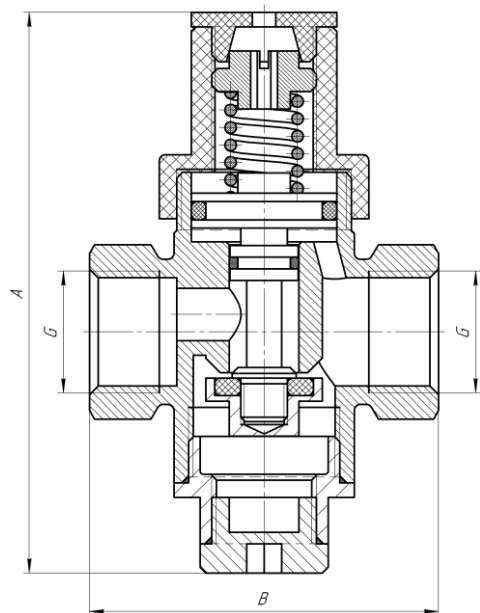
Габаритные и присоединительные размеры изделия.
